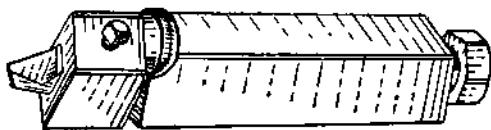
б. Резьбовой резец, заточенный по углу подъема винтовой линии
